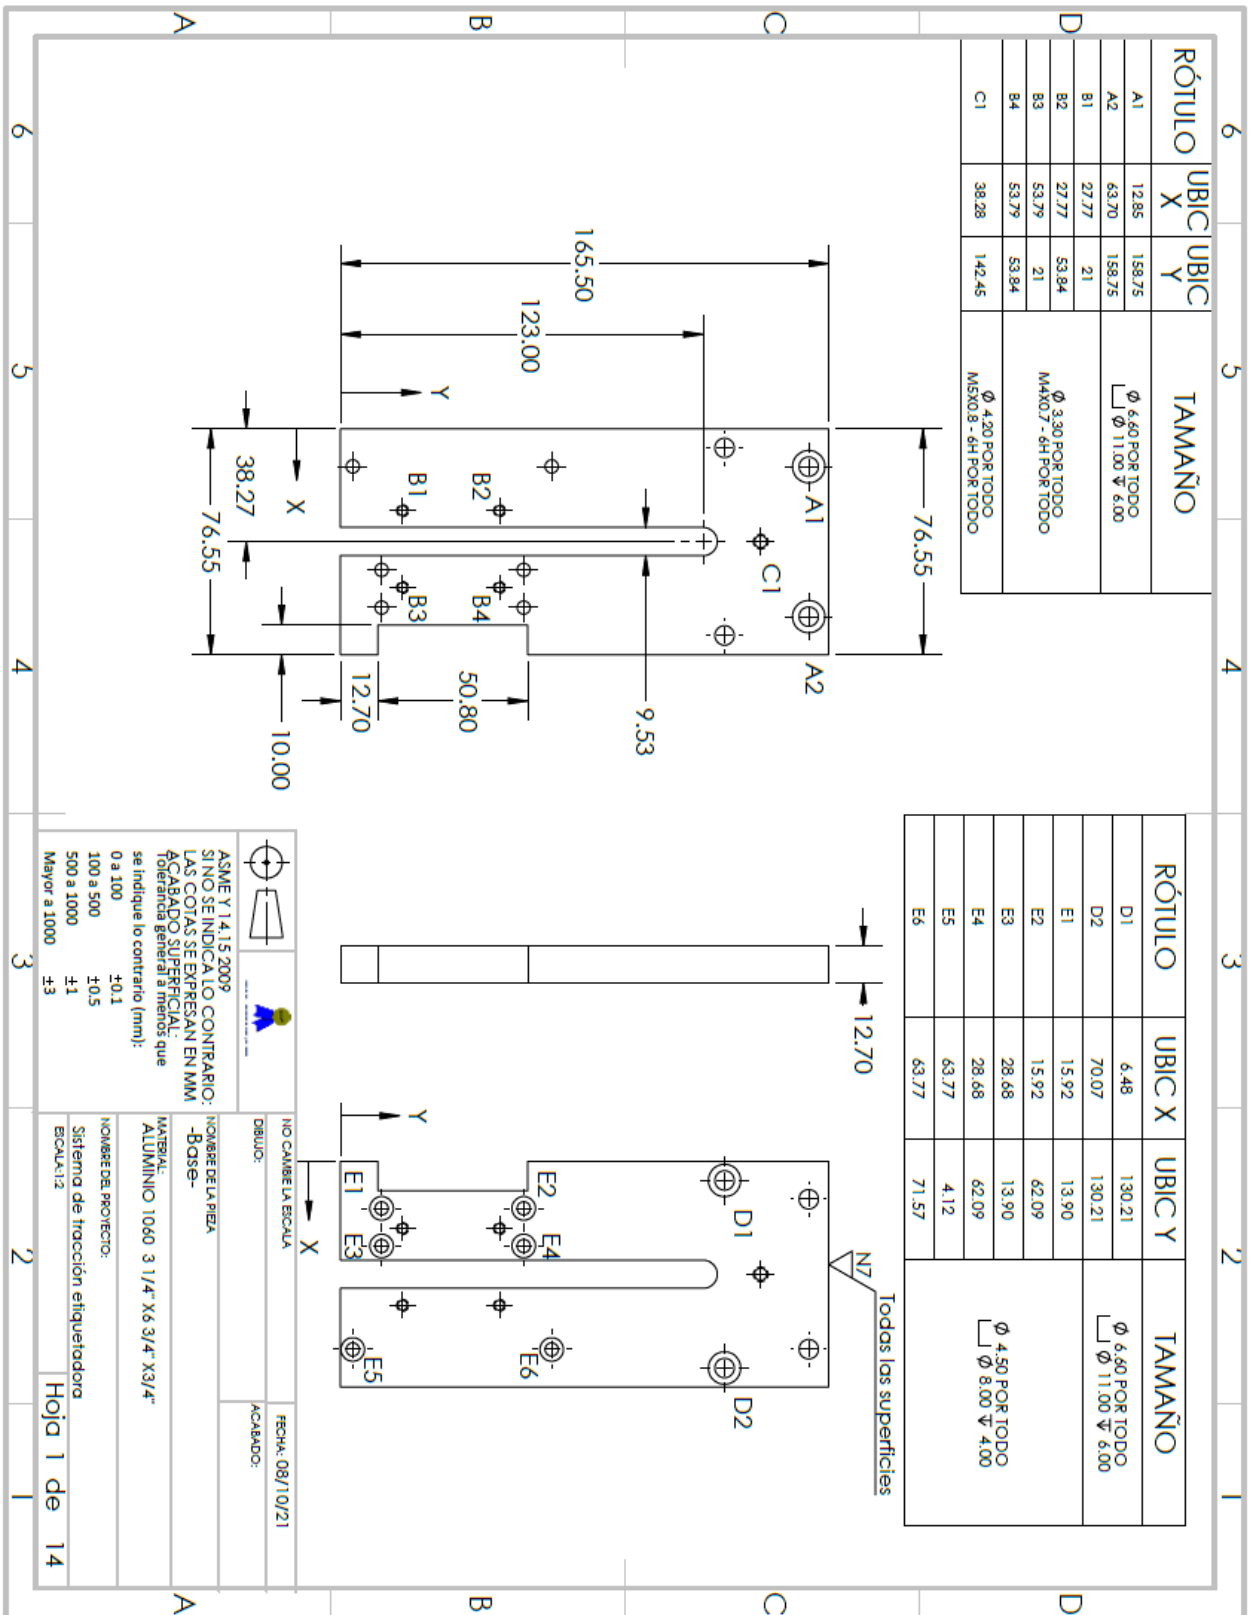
Plano de fabricación de la base del sistema de tracción para etiquetadora
